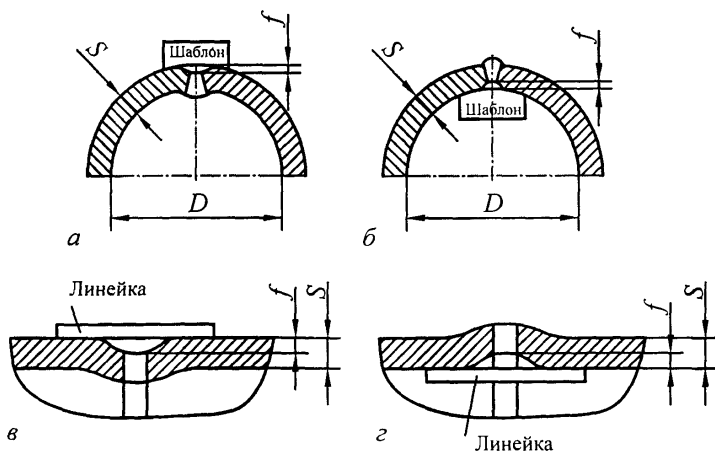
Контроль увода кромок продольных и кольцевых сварных соединений
